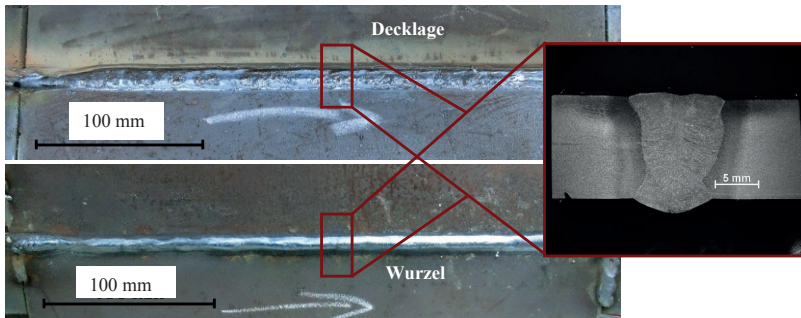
Einseitig in zwei Lagen ausgeführte Schweißnaht
